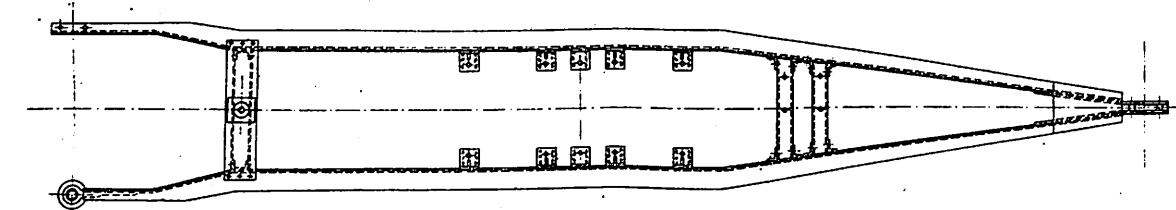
Geschweißter Motortragrahmen für eine 150 PS dieselmechanische Maschinenanlage.
